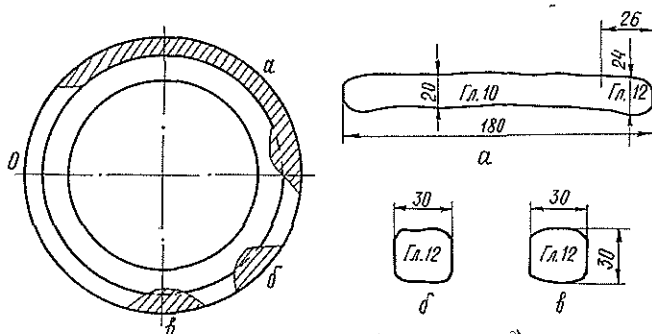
Выборка металла сварного шва штуцера коллектора
